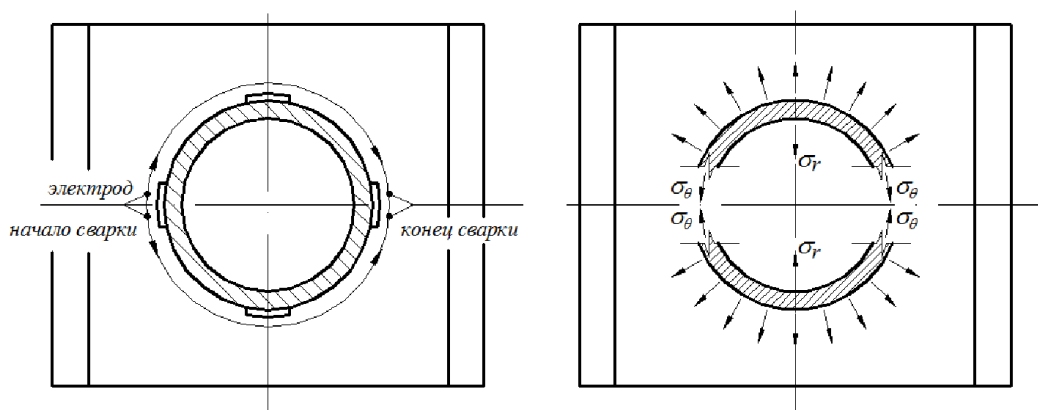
Сварной неповоротный стык трубы с основанием
